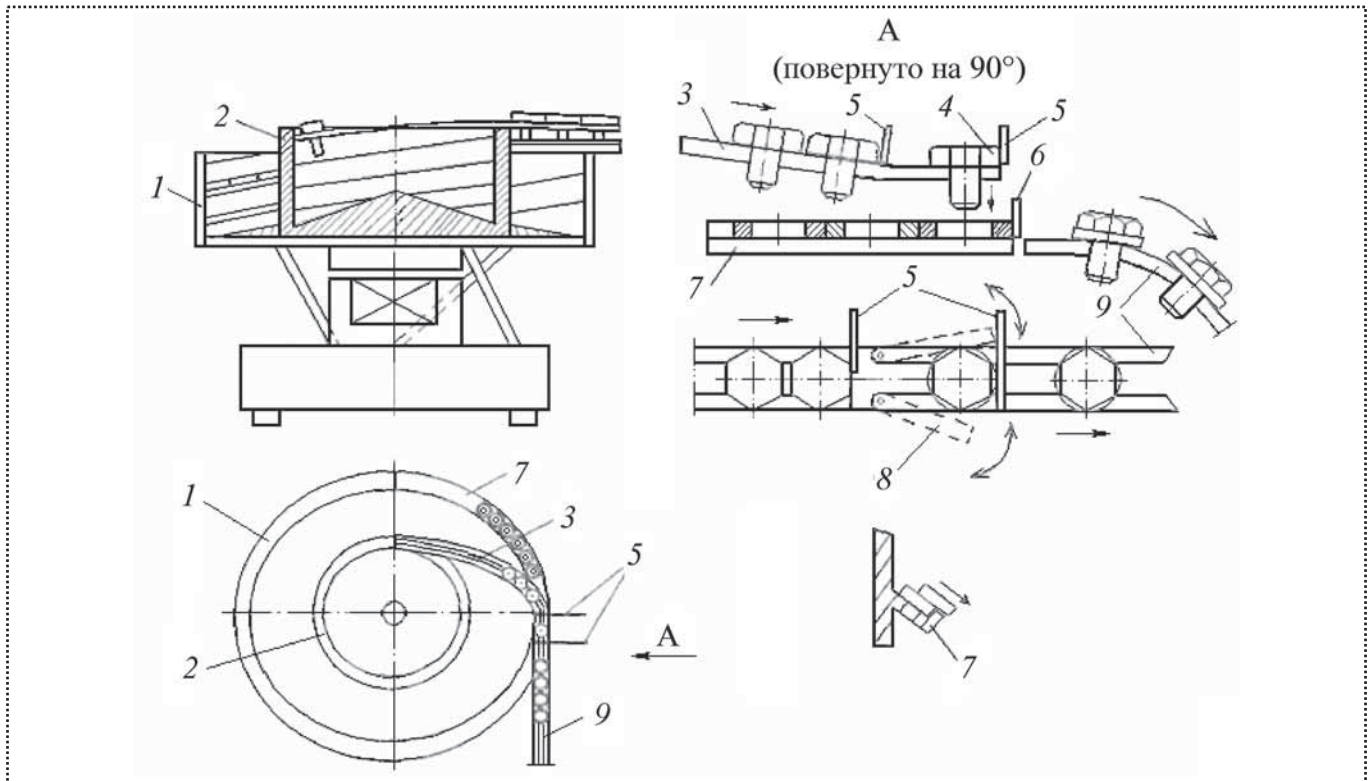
Схема вибробункера с двойной чашей для сборки болтов с шайбами:
